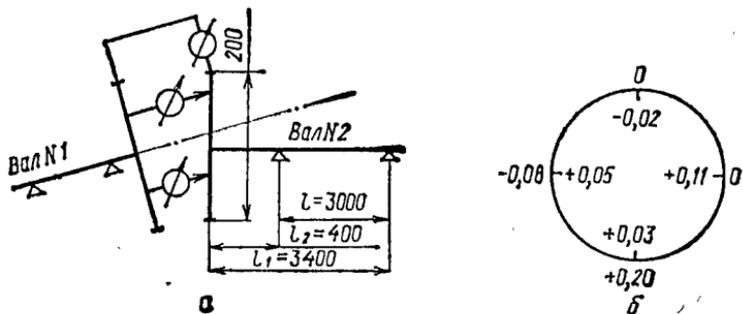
Центровка роторов с помощью трех индикаторов: а — схема центровки; б — карта измерений
